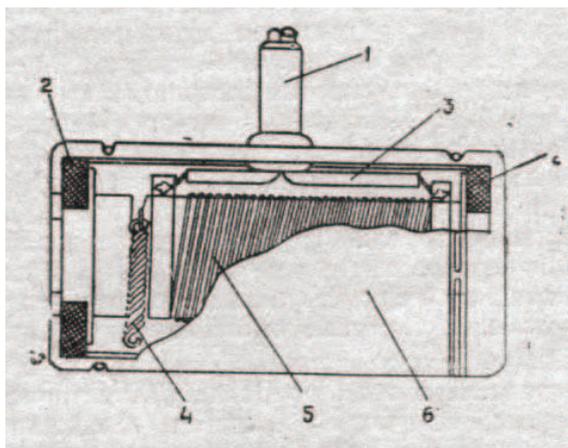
Схема электрического подогревателя для йодной трубки: 1 – втулка; 2 – прокладка; 3 – провод сетевой двухжильный; 4 – пружина; 5 – обмотка; 6 – корпус
